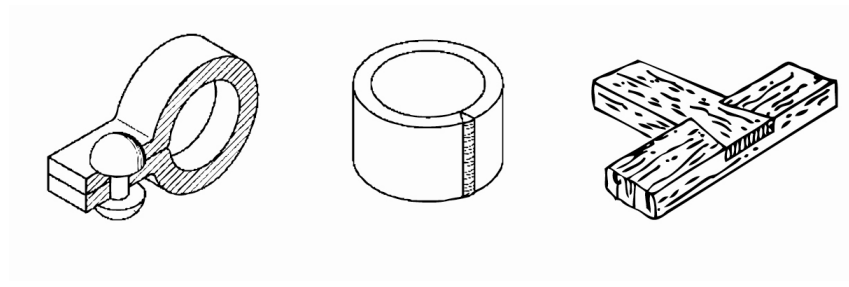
União rebitada, união soldada e união por sambladura.
